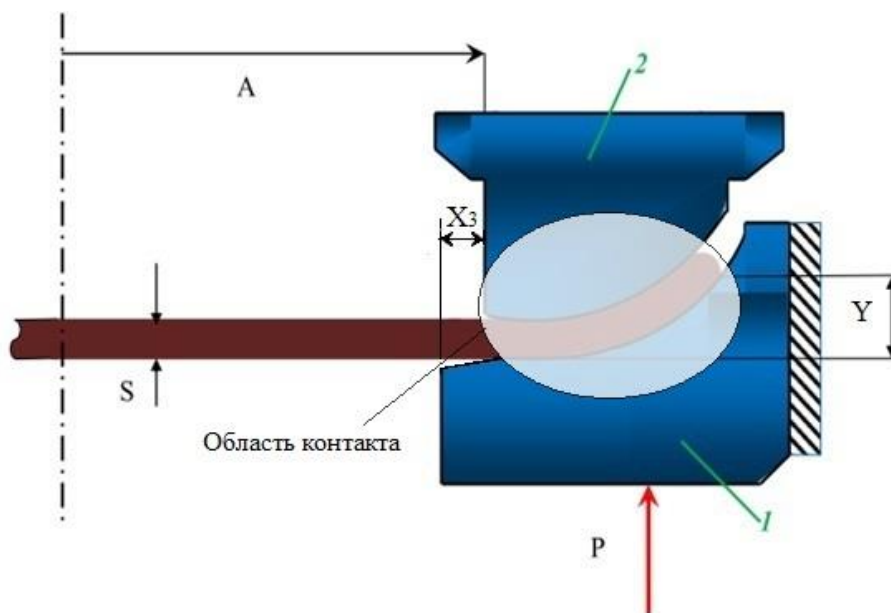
Схема настройки рабочего инструмента ППК
